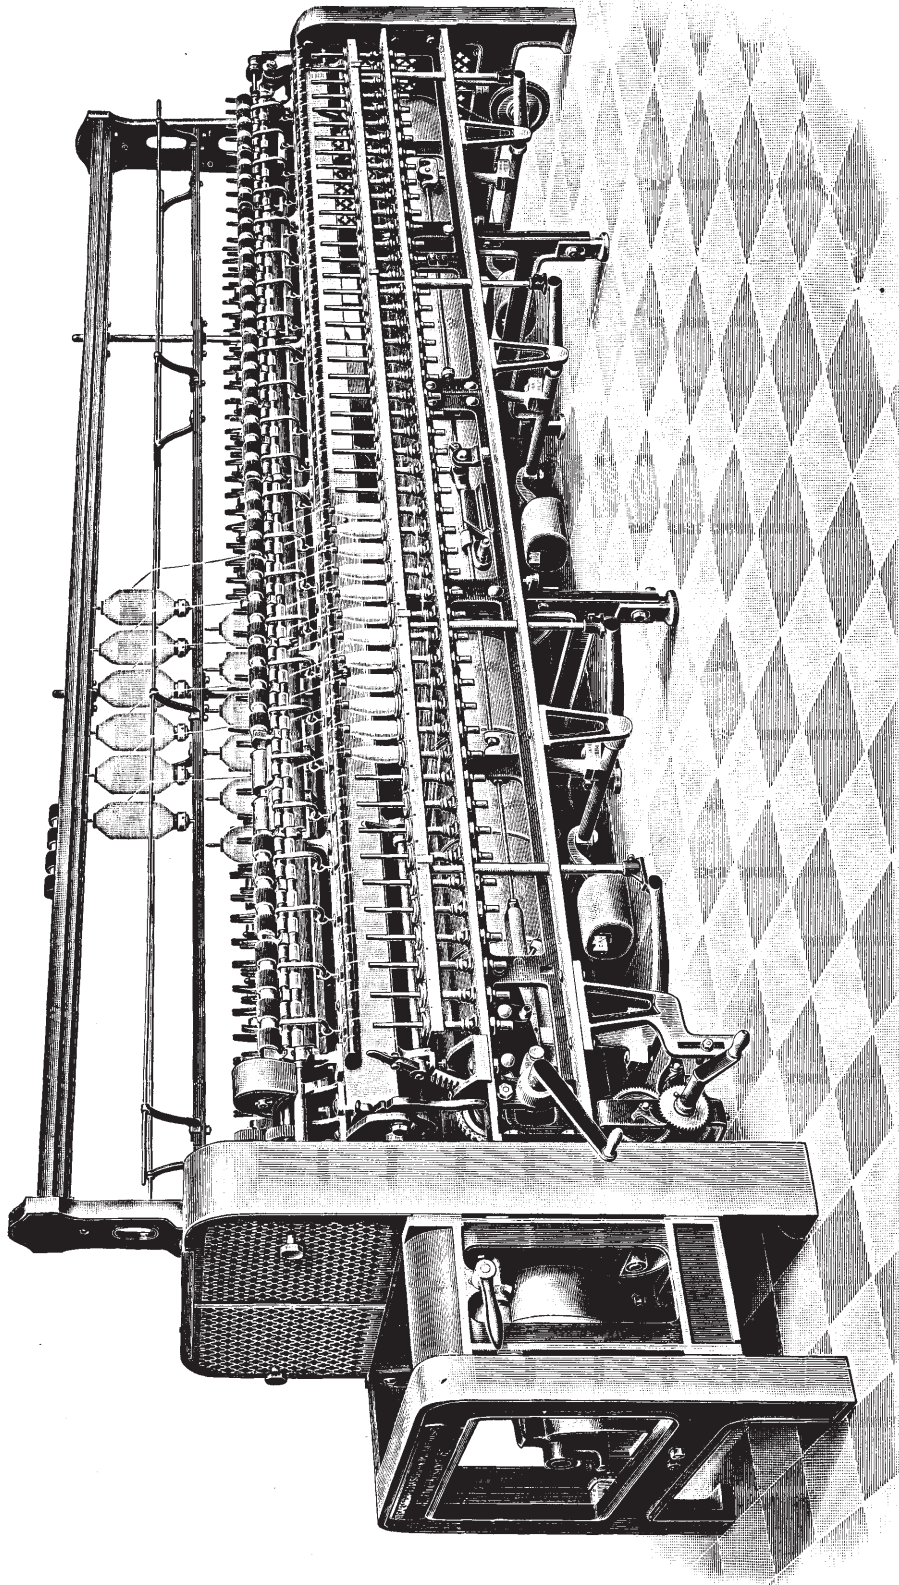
Ringspinnmaschine. Elsässische Maschinenbaugesellschaft.
